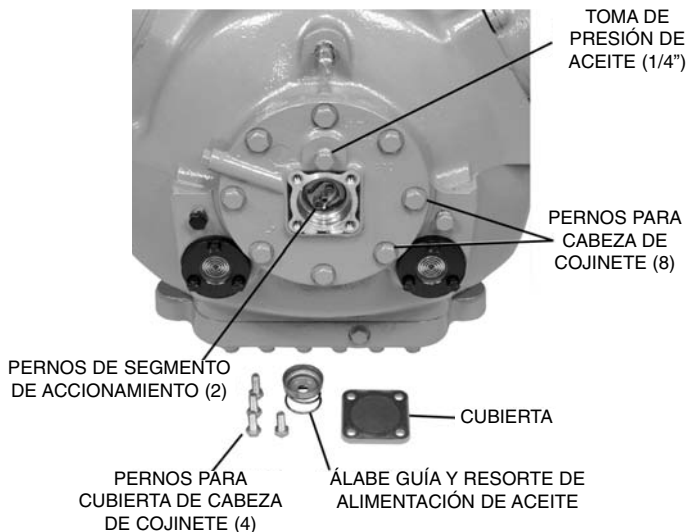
Cómo Retirar la Cabeza de Cojinete del Extremo de Bomba (Compresor 06E)
